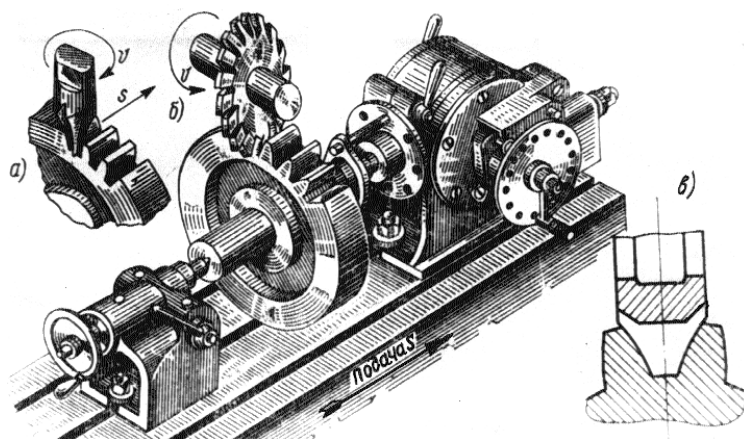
Обробка зубів методом копіювання: а – пальцевою фрезою; б, в – дисковою фрезою; 1 – ділильна головка
